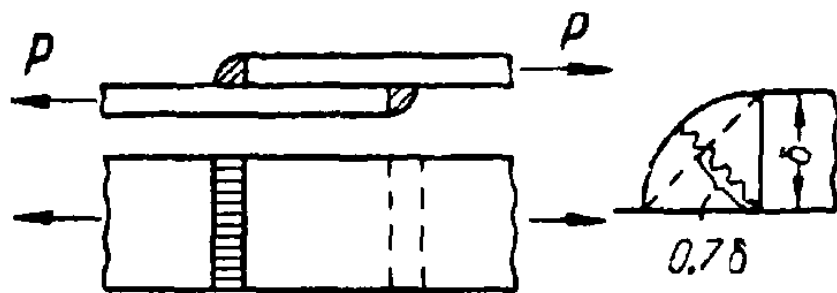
Сварное соединение с лобовыми швами.
